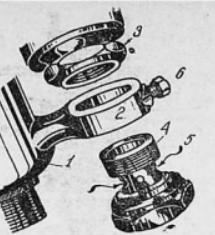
Крепление поплавковой камеры к корпусу карбюратора
